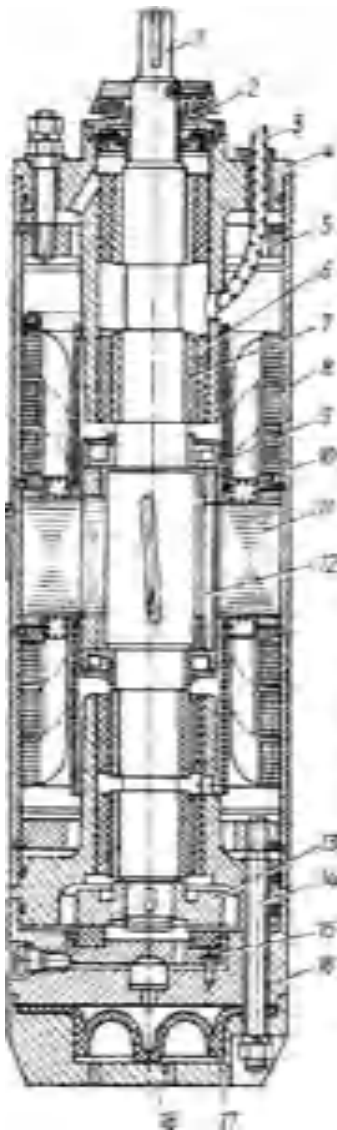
Конструктивний розріз заглибного електродвигуна ПЭДВ-28-140:
